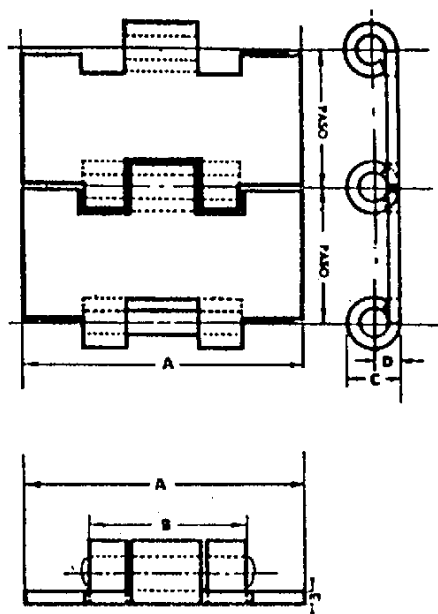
Vista de frente, planta y costado de una cadena plana articulada.
